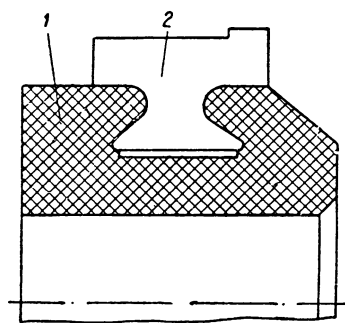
Коллектор новой конструкции тахометрического агрегата:
